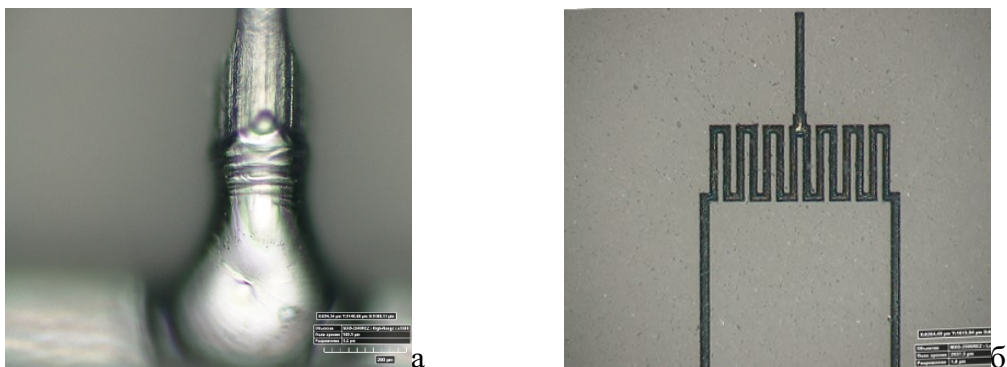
а) - изображение сварной точки в месте приваривания керна к проволочному подогревателю микрокатода (x 1500); б) - общий вид микрокатода, изготовленного с применением ЛПМ из фольги WRe-27 (увеличение x 100)
